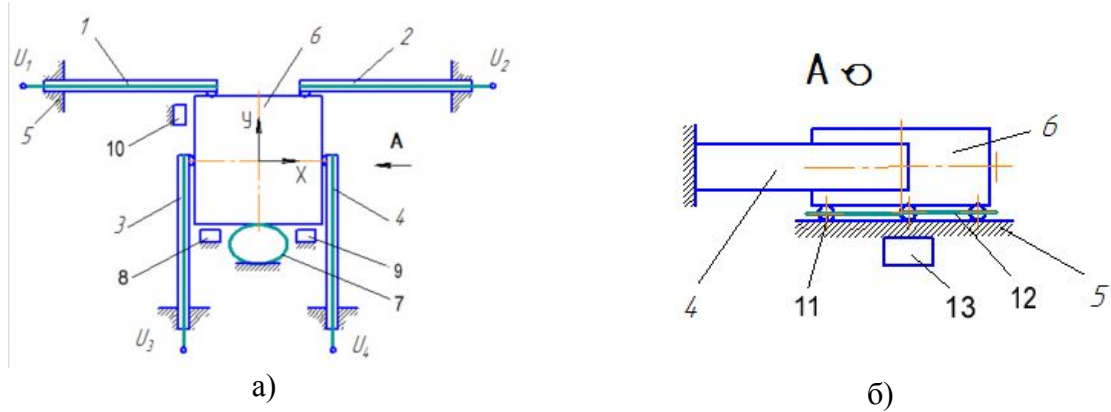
Схема двухкоординатного столика: а) вид сверху, б) вид по стрелке А
